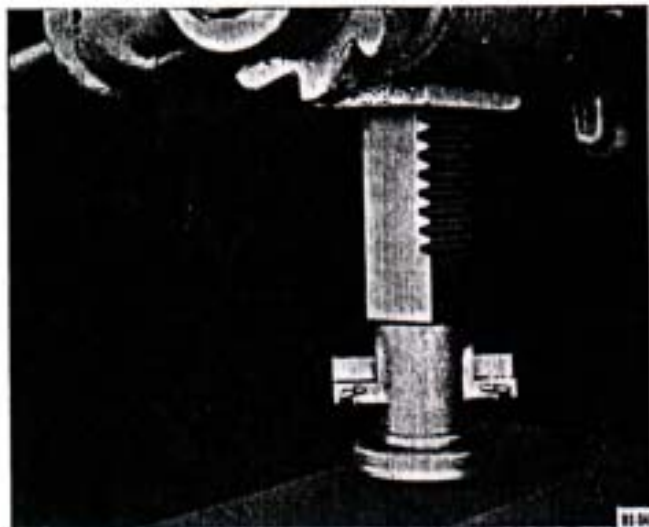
Instalando el cojinete de desembrague en el manguito de desembrague.
